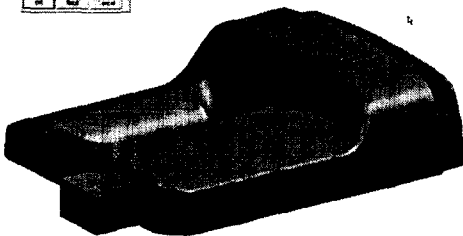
Cutting Patch 에 의한 extrude body 의 trim
